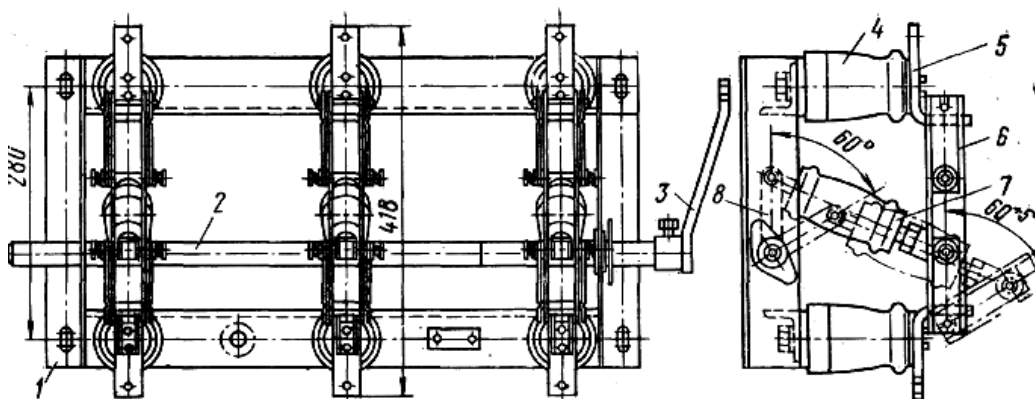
Розмикач РВ-10: 1 — рама; 2 — вал; 3 — важіль; 4 — опорний ізолятор; 5 — нерухомий контакт; 6 — ніж; 7 — тяга з ізолятором; 8 — важіль
